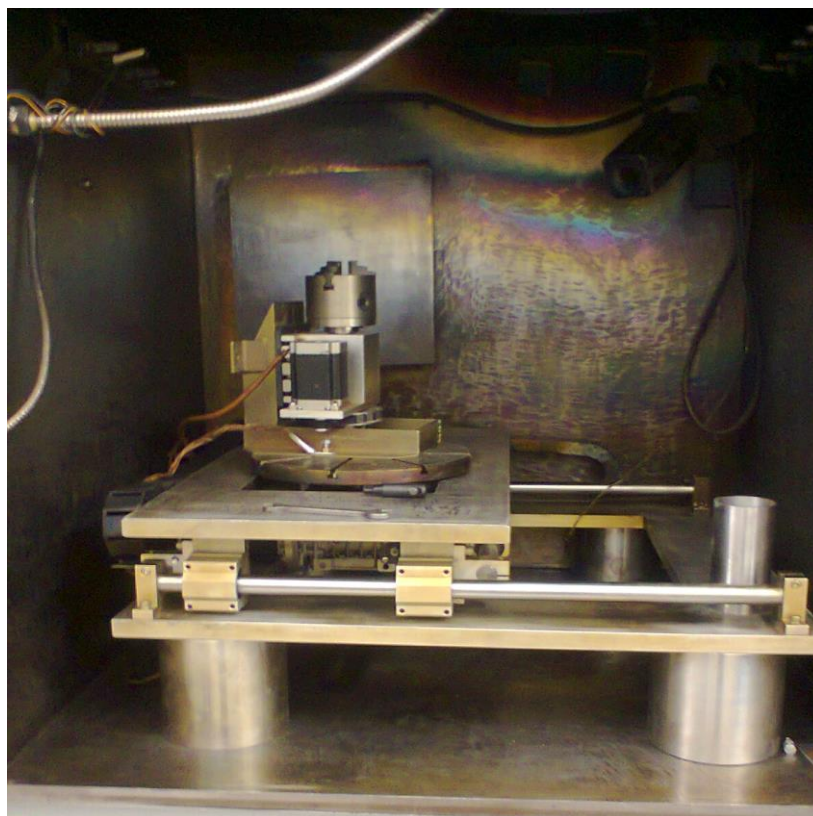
Манипулятор перемещения с установленной планшайбой и дополнительными приспособлениями
